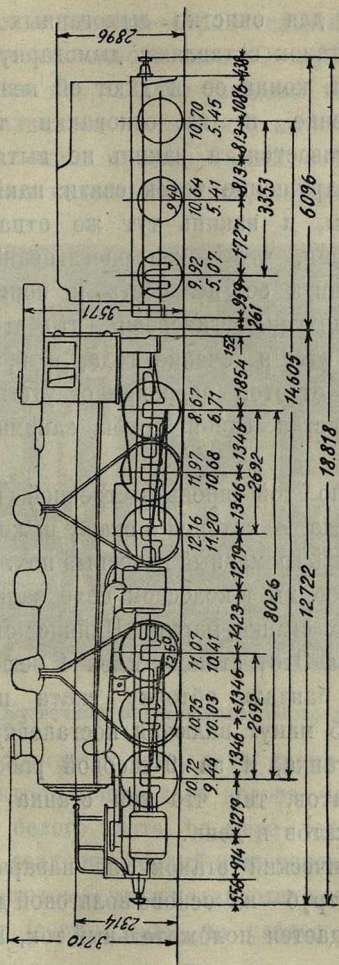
Товарный паровоз с двойной машиной (с указанием главных размеров).
